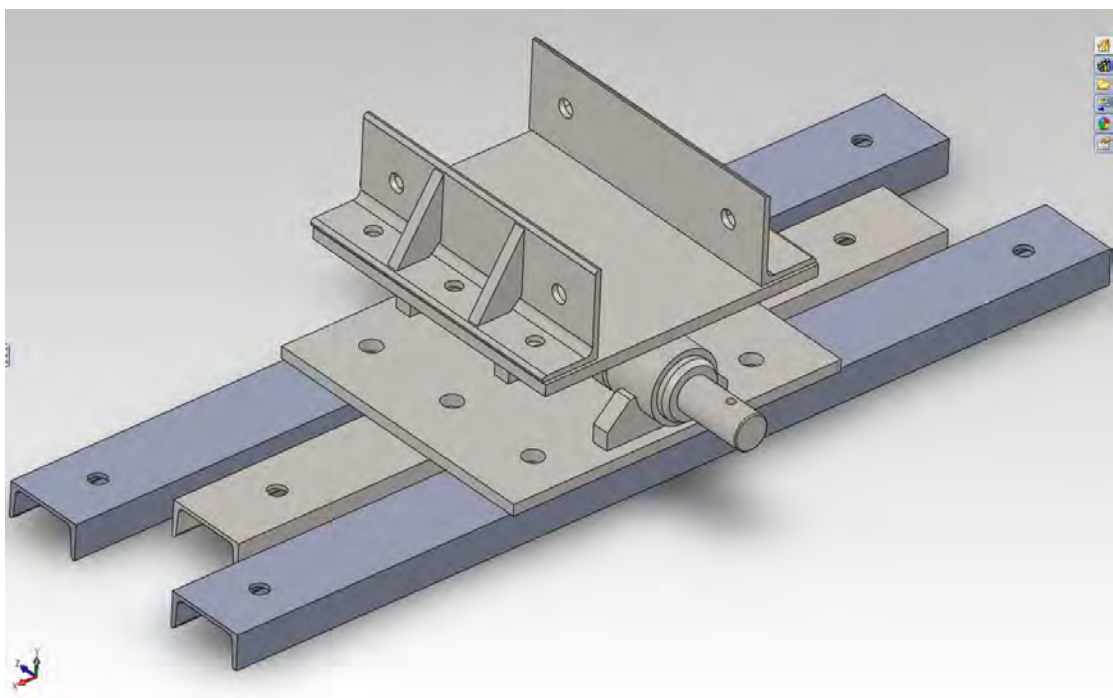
Vista assieme cerniera di base e profili di collegamento.
